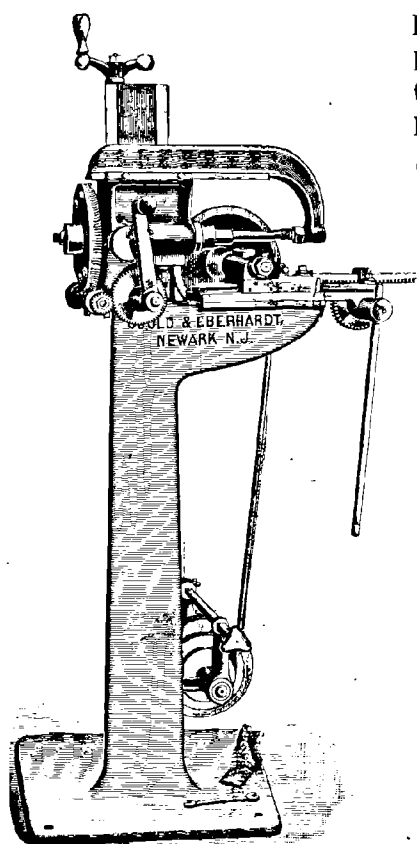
Machine Gould-Eberhardt à tailler les engrenages à la main.
